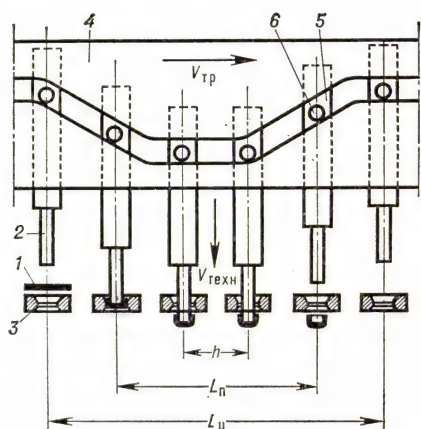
Схематическая развёртка пресовой операции на роторной линии: 1 — предмет обработки; 2, 3 — инструмент; 4 — пазовый копир; 5 — ползун; 6 — ролики ползунов; L_p — шаг между предметами обработки; L_c — длина пути предмета обработки; L_c — цикловой путь инструмента; $v_{тр}$ — транспортная скорость; $v_{техн}$ — технологическая скорость.
